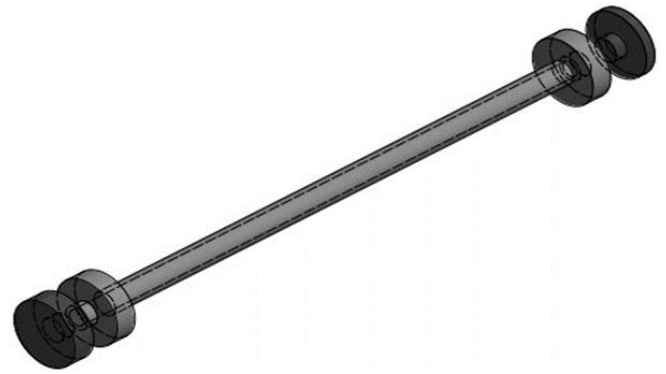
Vista explodida do modelo tridimensional do tubo de choque com flanges.
